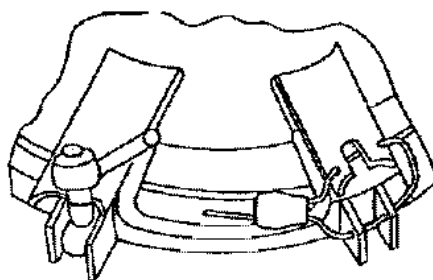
Схема установки универсального ЗПУ с длиной каната 500 мм на верхней крышке загрузочного люка цистерны барашкового типа при отсутствии пломбировочных проушин в место одного снятого барашка
